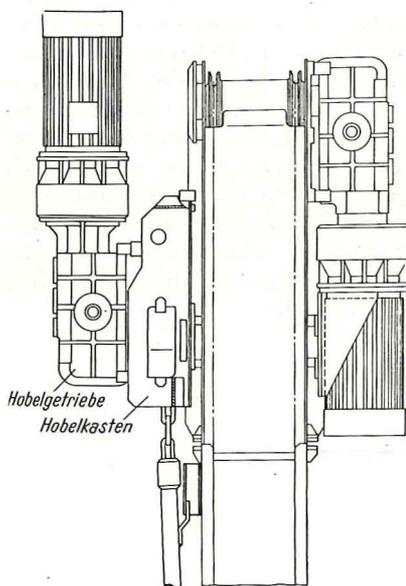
Installation du rabot appliqué avec commande unique du transporteur et commande du rabot par engrenages coniques. Hobelgetriebe = commande du rabot - Hobelkasten = carter du rabot.
